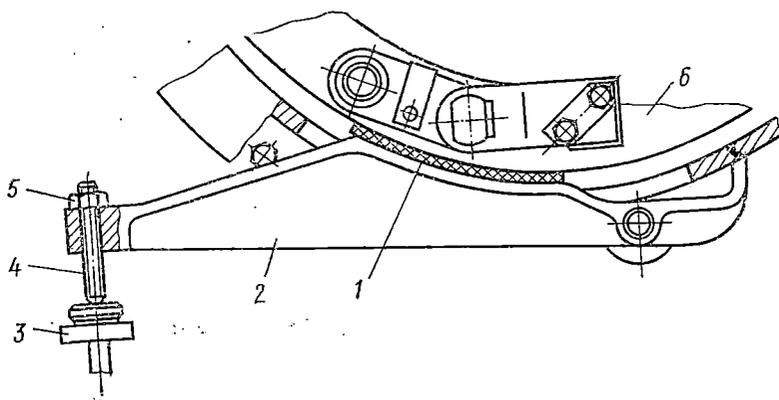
Тормозок муфты сцепления экскаватора Э-652Б:
